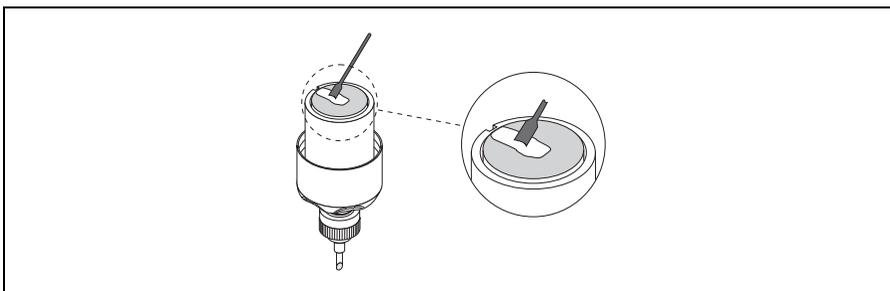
Enduire les surfaces de contact du capteur avec du produit de couplage
